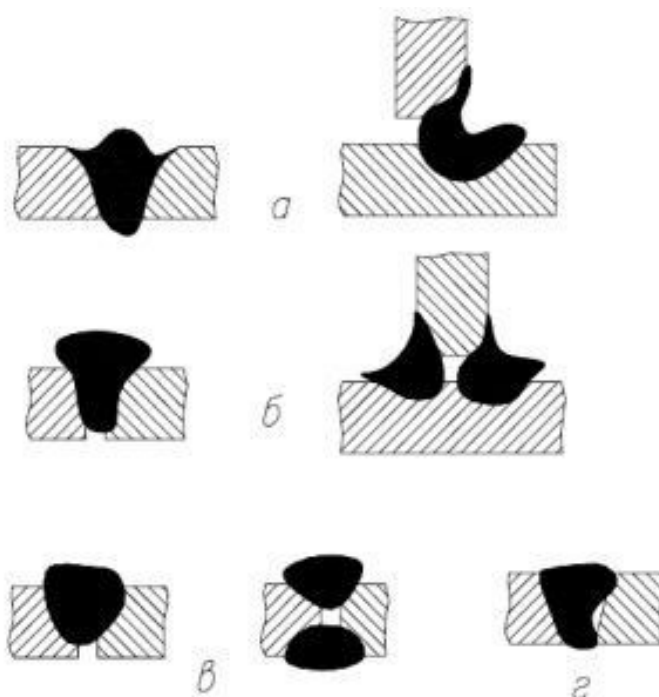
Дефекты при сварке плавлением: а – подрез; б – наплыв;
